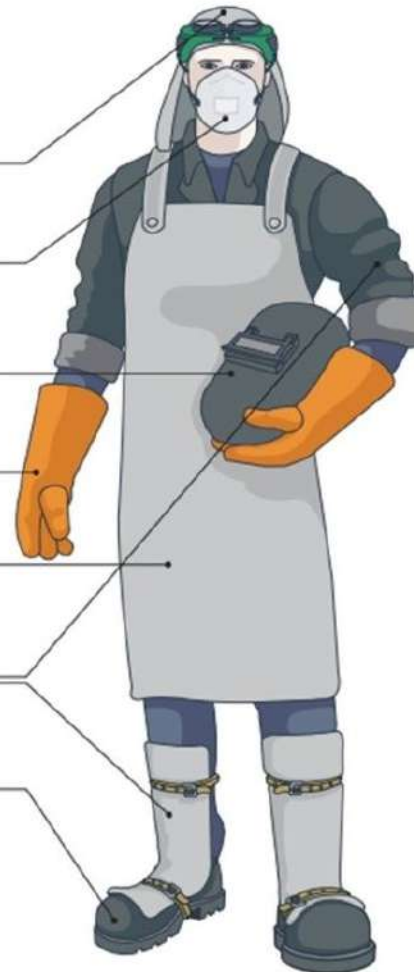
EPIS para soldadura, Fuente: "Aubert Suministros Industriales (Web).
